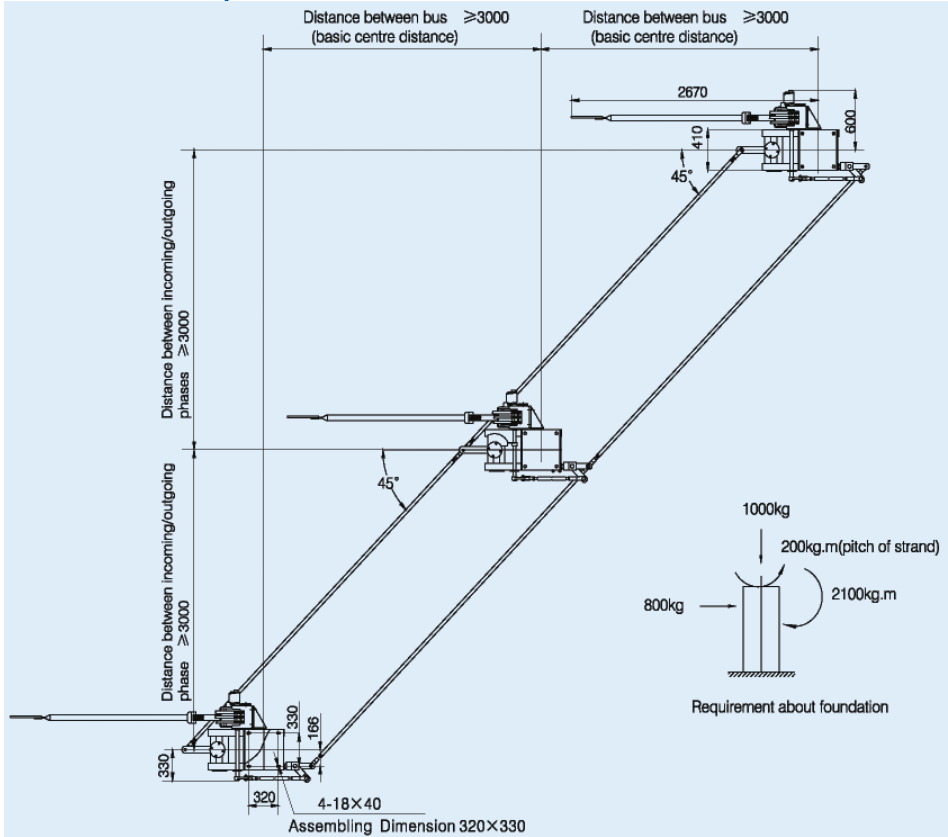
Внешний вид и размеры разъединителя GW22-252
